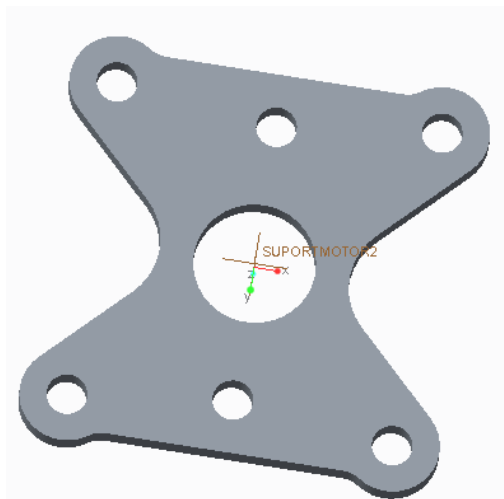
Dibuix 3D placa per collar l'adaptador dels motors al braç.
